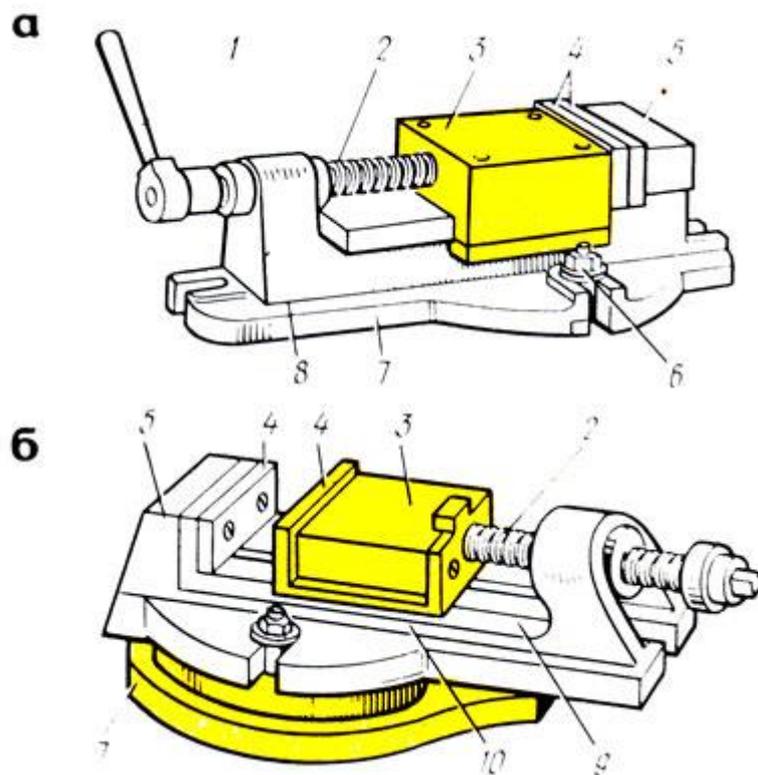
Слесарные тиски: а - не поворотные, б - поворотные
